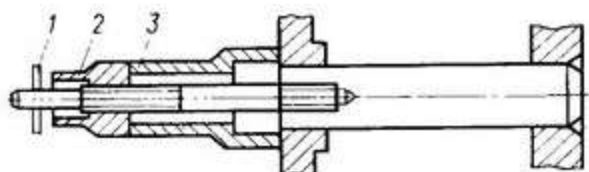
Съемник для выпрессовки оси блока шестерен заднего хода
